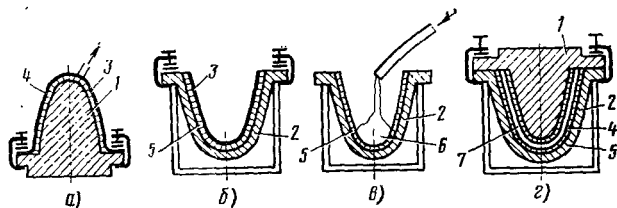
Схема изготовления трехслойного обтекателя с пенозаполнителем: а, б, в, г — последовательность этапов (1 — пуансон; 2 — матрица; 3 — резиновый чехол; 4 — внутренняя обшивка; 5 — внешняя обшивка; 6 — жидкая композиция; 7 — пенопласт)
